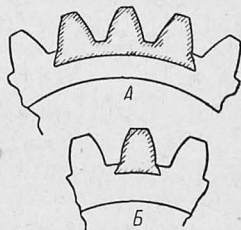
а—вставка трех зубьев; б—вставка одного зуба
